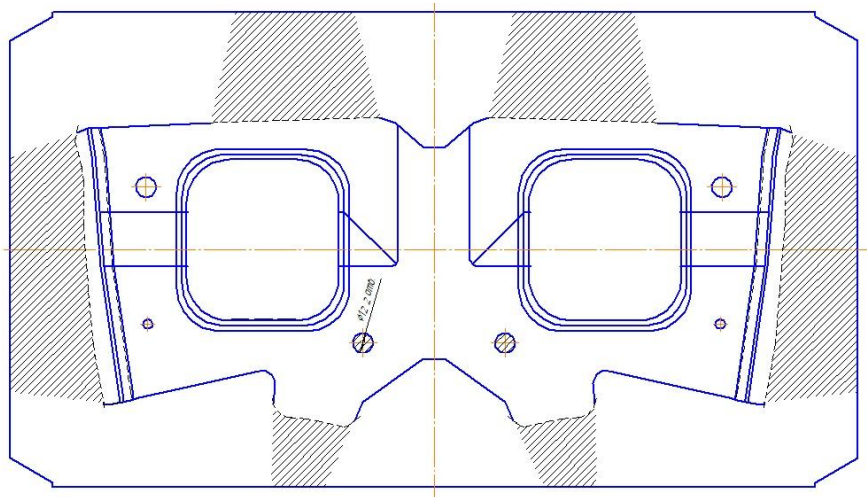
Обрезка 2-я, пробивка 2-я
